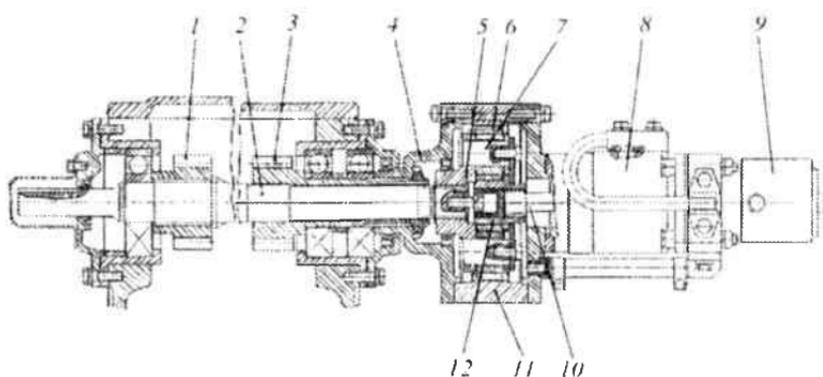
Гидравлический дифференциальный механизм поворота: 1 и 3 – зубчатые колеса; 2 – карданный вал; 4 – ступица; 5 – водило; 6 – сателлиты; 7 – ось сателлита; 8 – гидромотор; 9 – золотниковый механизм; 10 – коронная шестерня; 11,12 – солнечные шестерни
